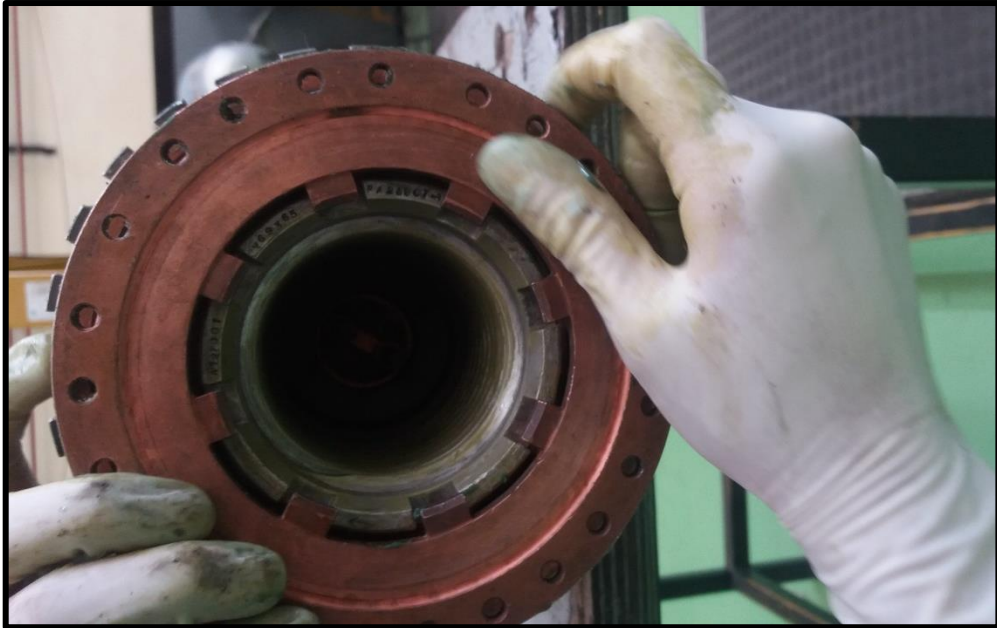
Montaje de los case assembly propeller en la Race center.
